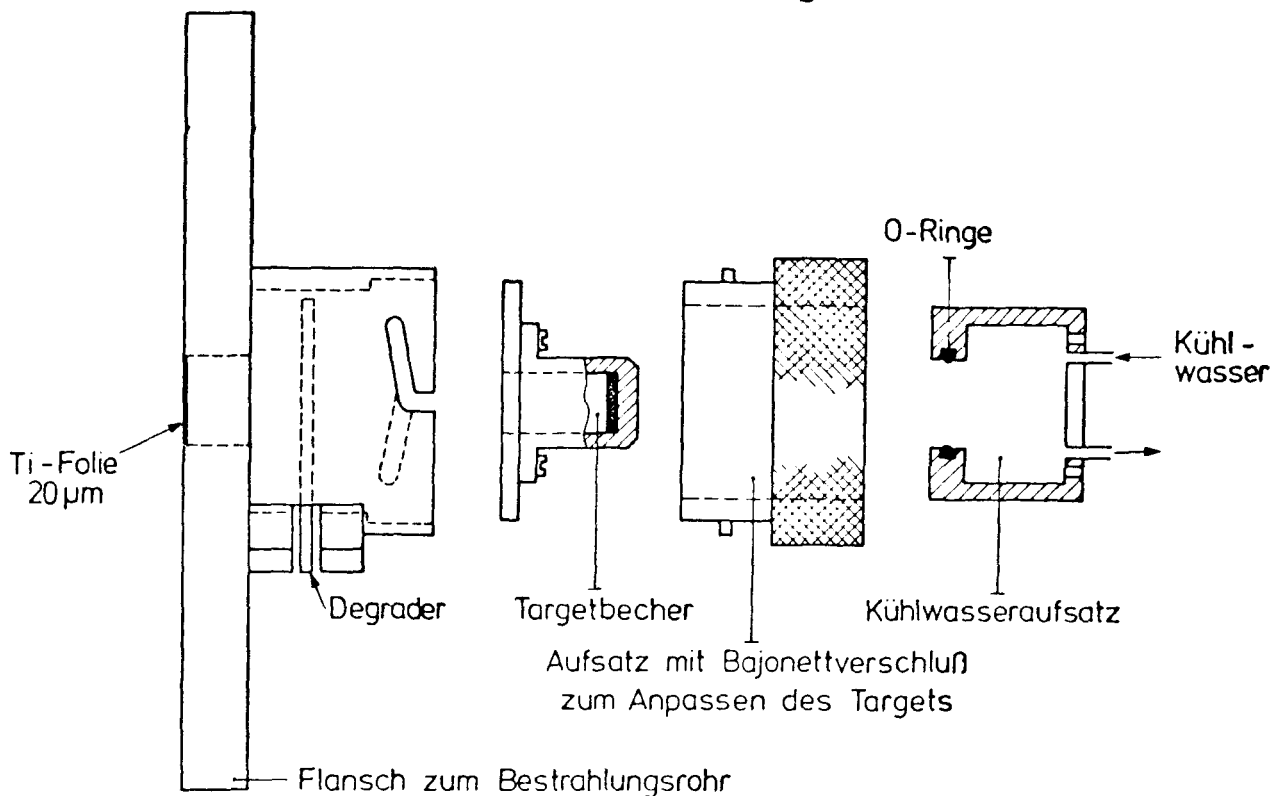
Wassergekühltes Target (Explosionszeichnung)
